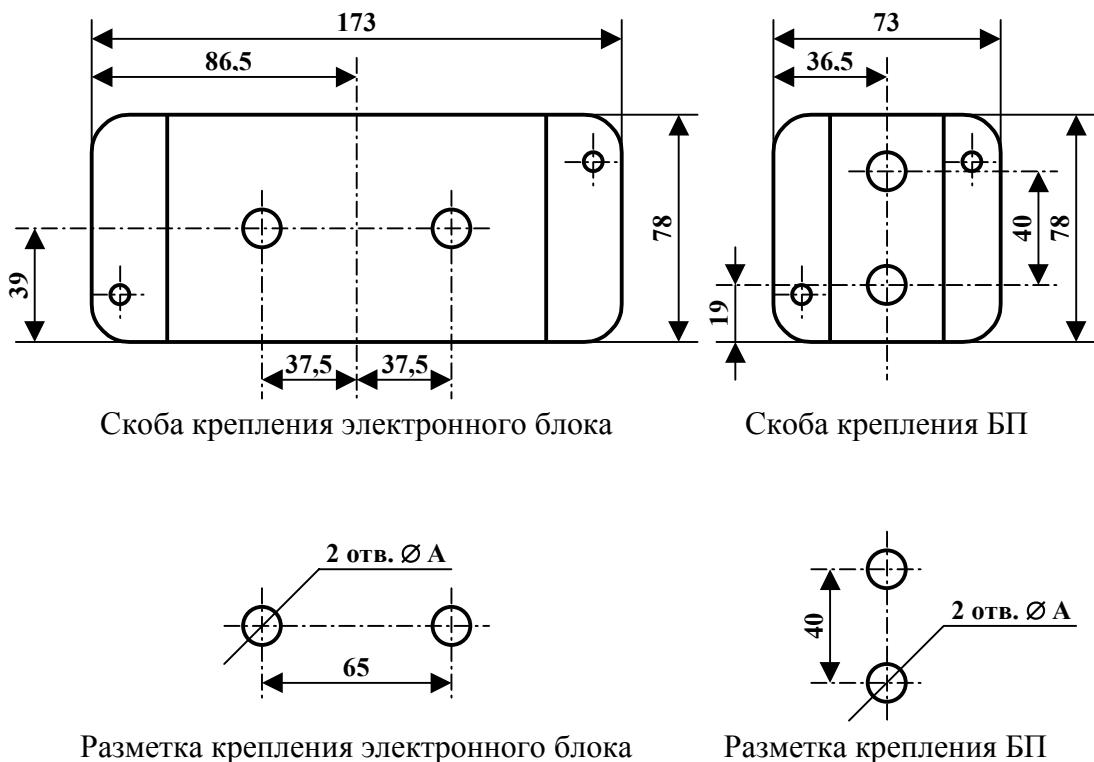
Разметка и габаритные размеры скоб крепления ЭБ и БП.
